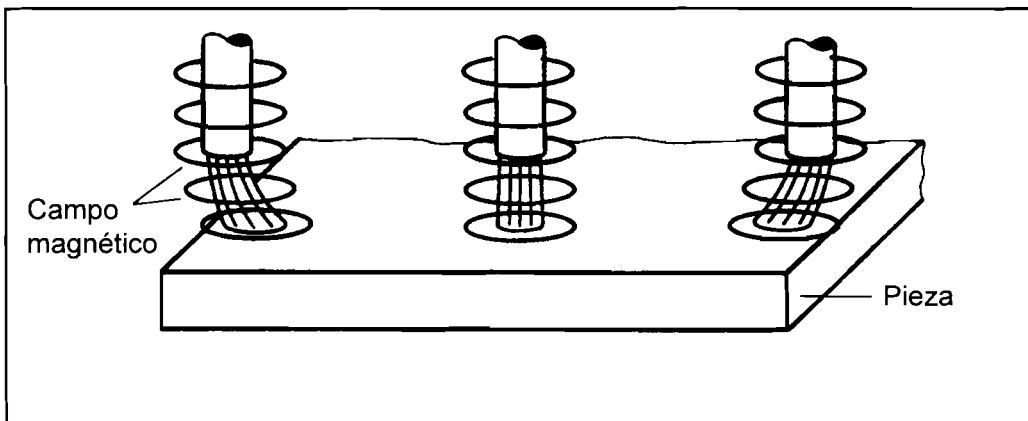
SOPLO MAGNÉTICO AL SOLDAR CERCA DE LOS EXTREMOS DE UNA PIEZA FERROMAGNÉTICA
